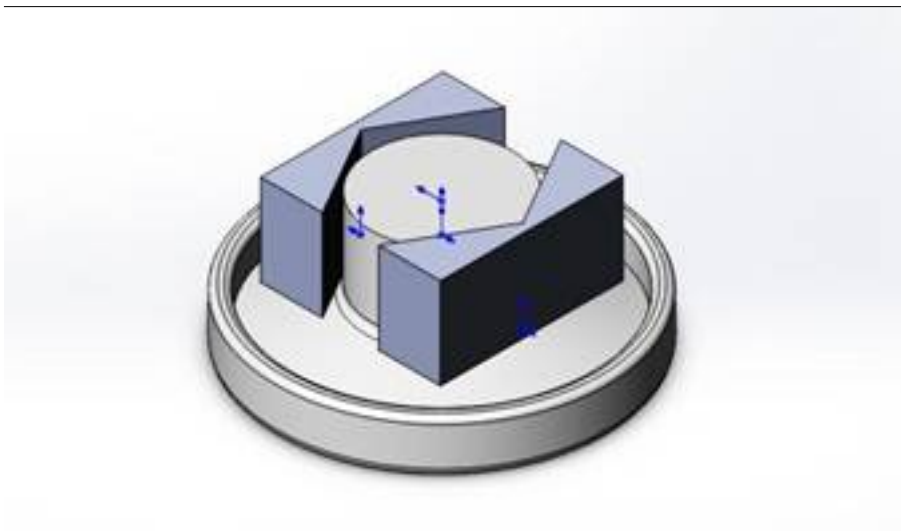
3D - сборка обрабатываемой детали с зажимными элементами
